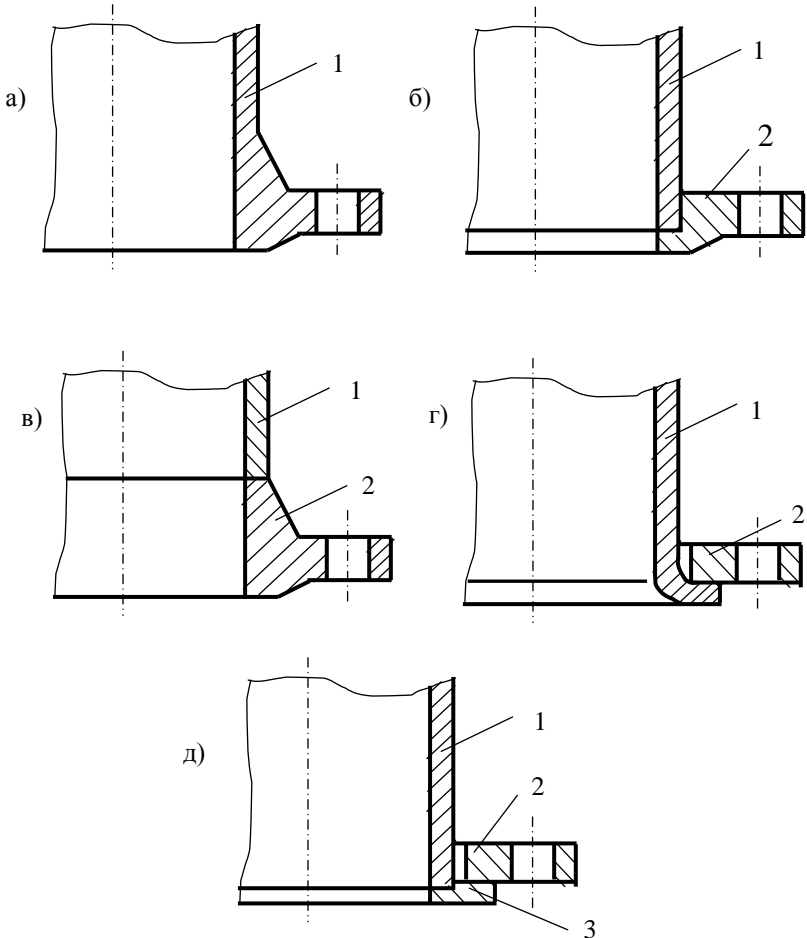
Конструктивное исполнение фланцев: а) литые или кованные заодно с трубой или элементом аппарата; б) плоские приварные; в) с втулкой приварные встык; г) свободные на отбортовке; д) свободные на приварном кольце. На схемах обозначено: 1 – элемент аппарата; 2 – фланец; 3 – приварное кольцо
